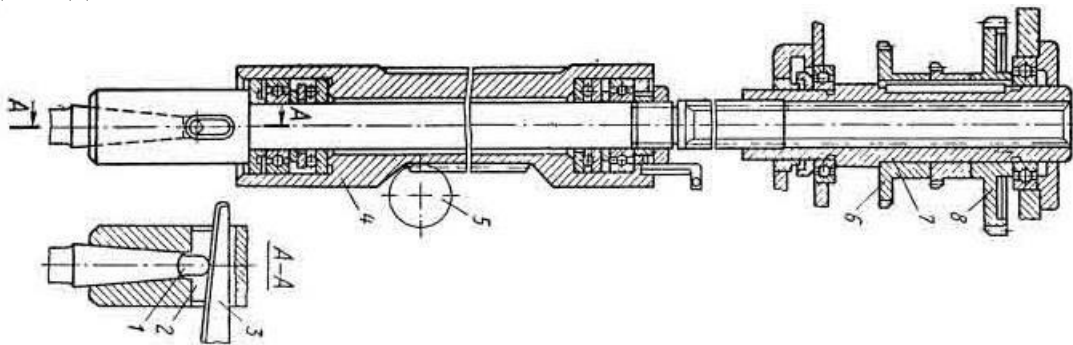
Шпиндель вертикально-свердлувального верстата 2Н150.
